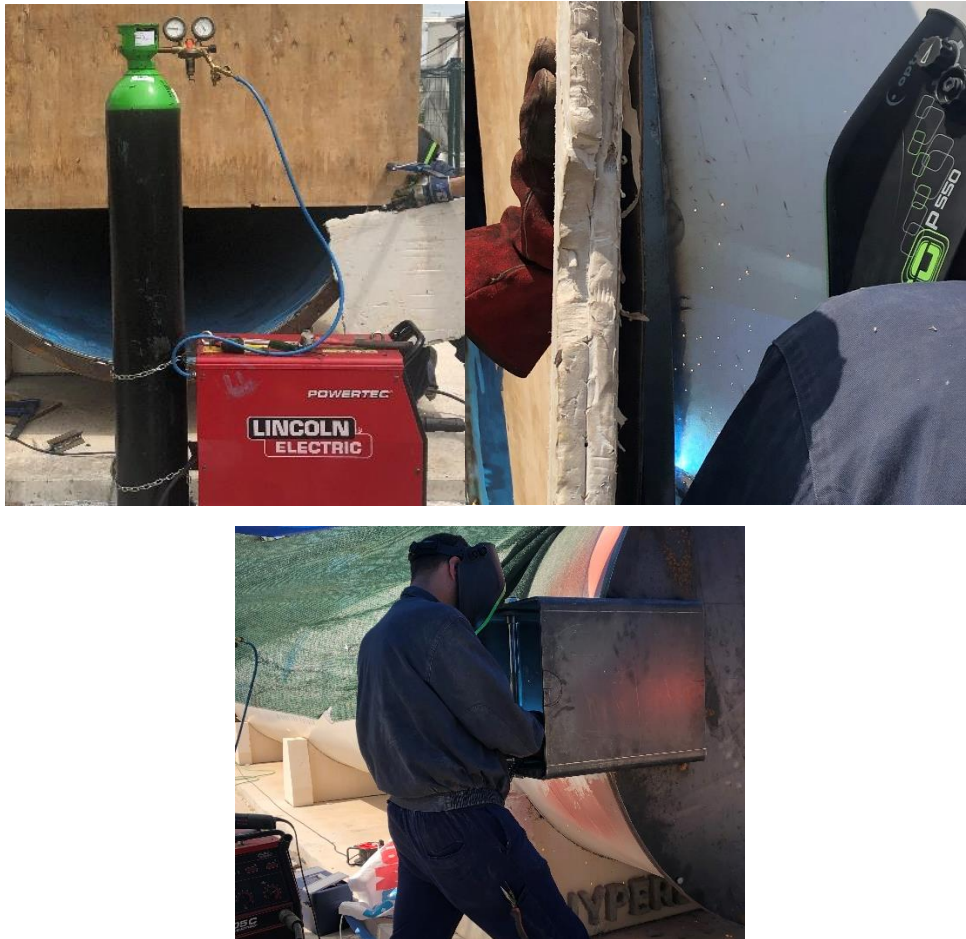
Trabajos de soldadura en el Hyper-Tube.
